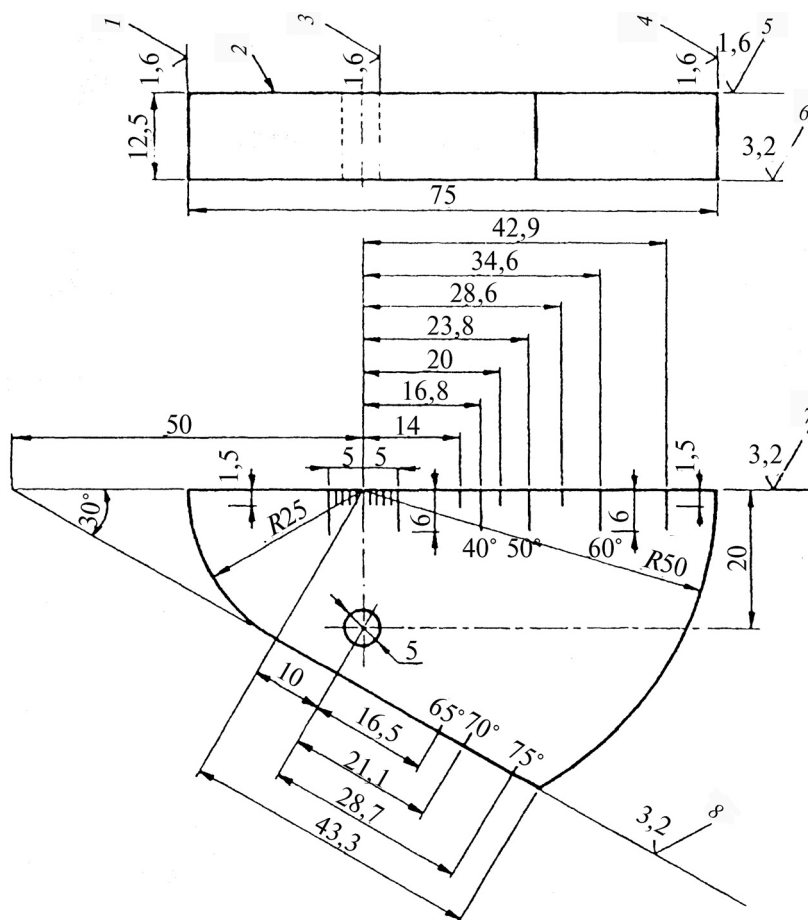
1 — шлифованная цилиндрическая поверхность; 2 — отражающая поверхность; 3 — обработанная поверхность отверстия; 4 — шлифованная цилиндрическая поверхность; 5 — шероховатость; 6, 7, 8 — фрезерованная поверхность
